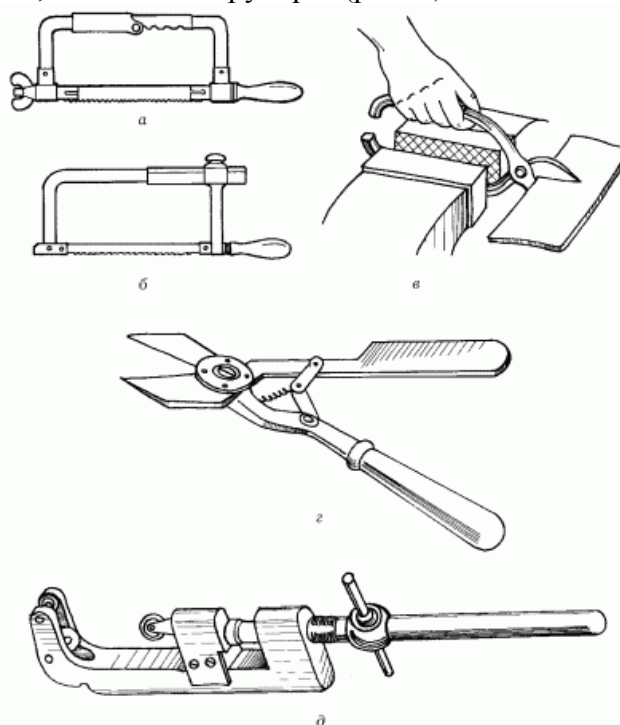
Инструменты для резки металла: а – ножовка; б – лобзик; в – ручные ножницы; г – силовые ножницы; д – труборез.
